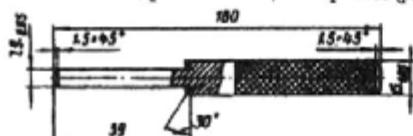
Оправка для выпрессовки и запрессовки направляющей втулки клапана
